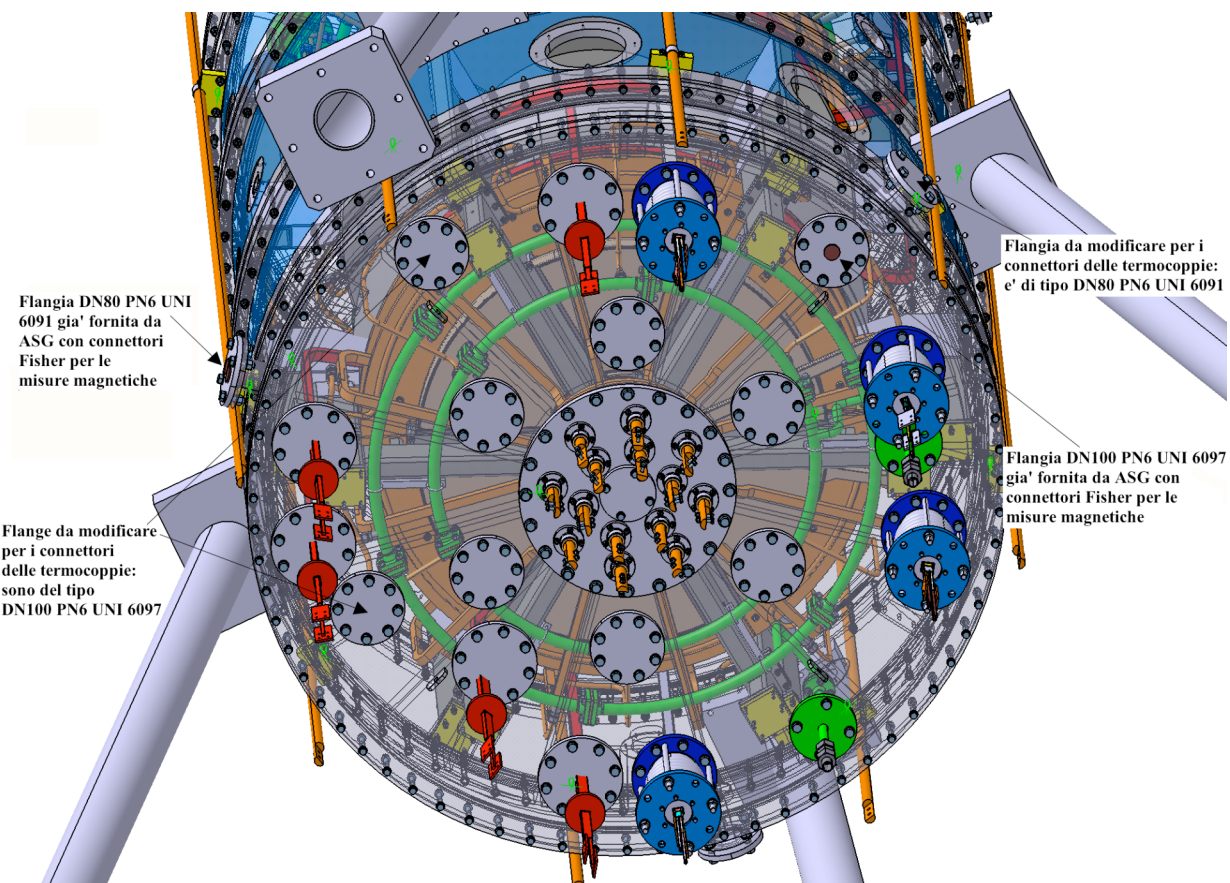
Parte inferiore del Load Assembly di Multi-Pinch/PROTO-SPHERA
